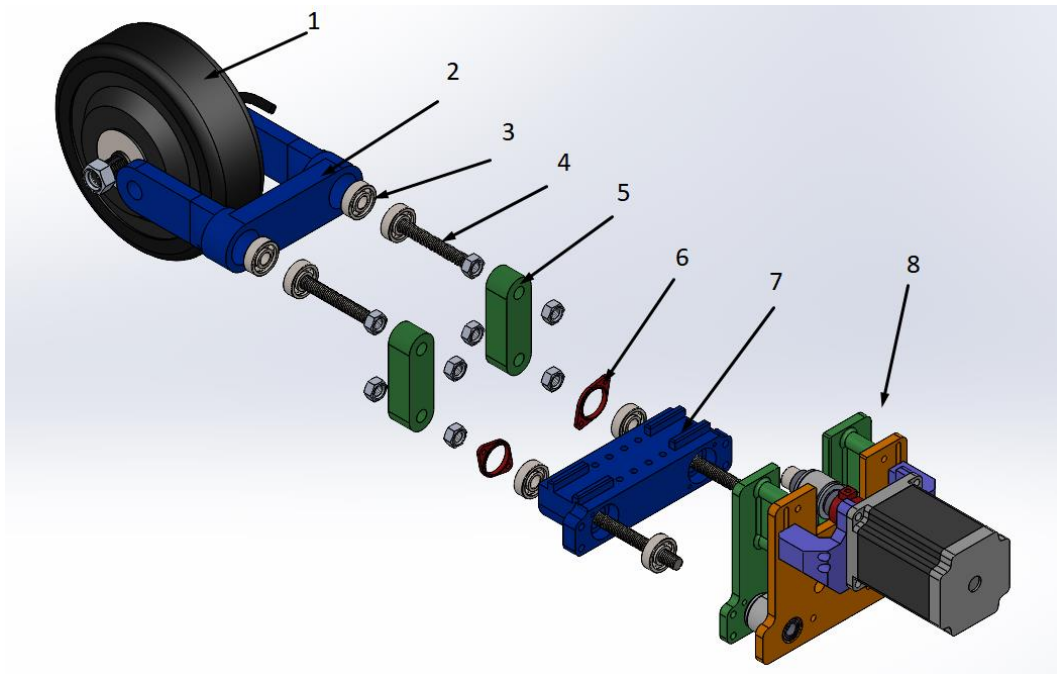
3D модель механізму балансування: 1) заднє приводне мотор-колесо; 2) вилка заднього колеса 3) підшипники серії 608; 4) шпильки M8x60; 5) кривошип; 6) кришки підшиніків; 7) корпус; 8) привід механізму балансування
